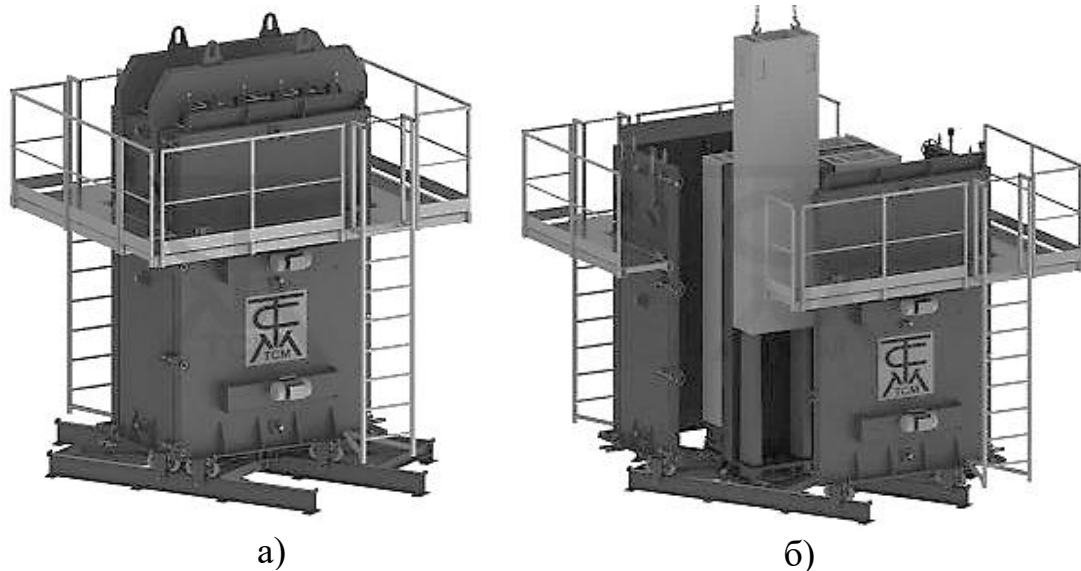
Стендова установка для виготовлення 4-х блоків:
